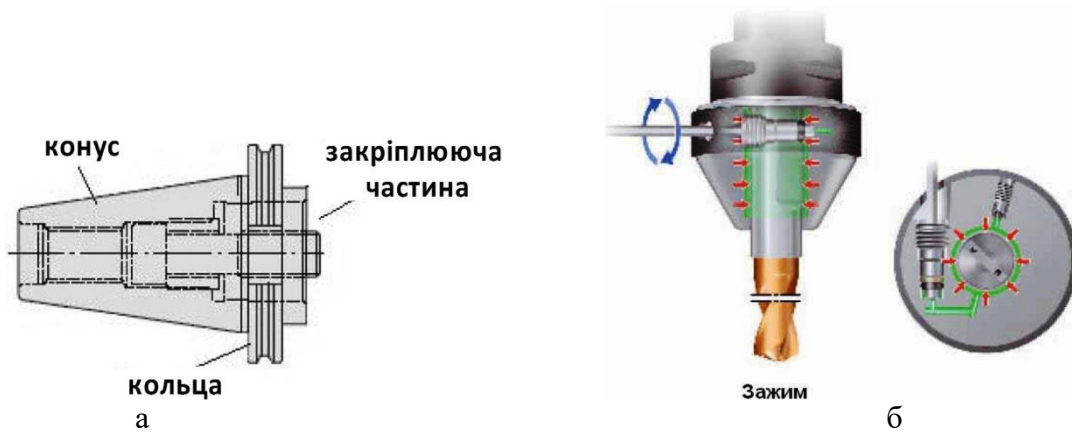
Фрезерна оправка (а) та оправка з гідропластом (б)
